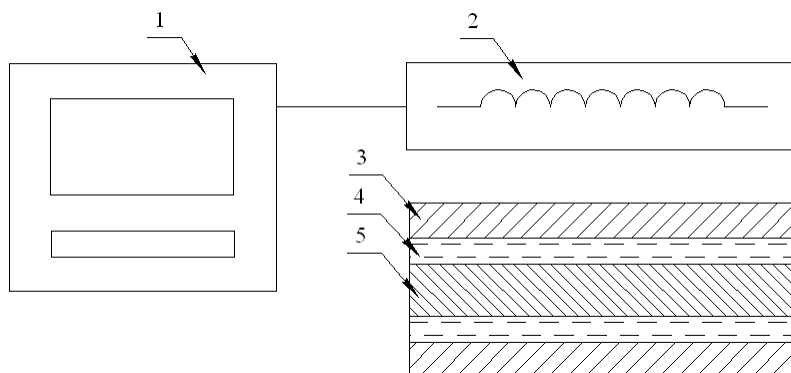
Схема индукционного нагрева: 1 – рабочая станция, 2 – индуктор, 3 – цилиндр, 4 - полимер, 5 – шнек
